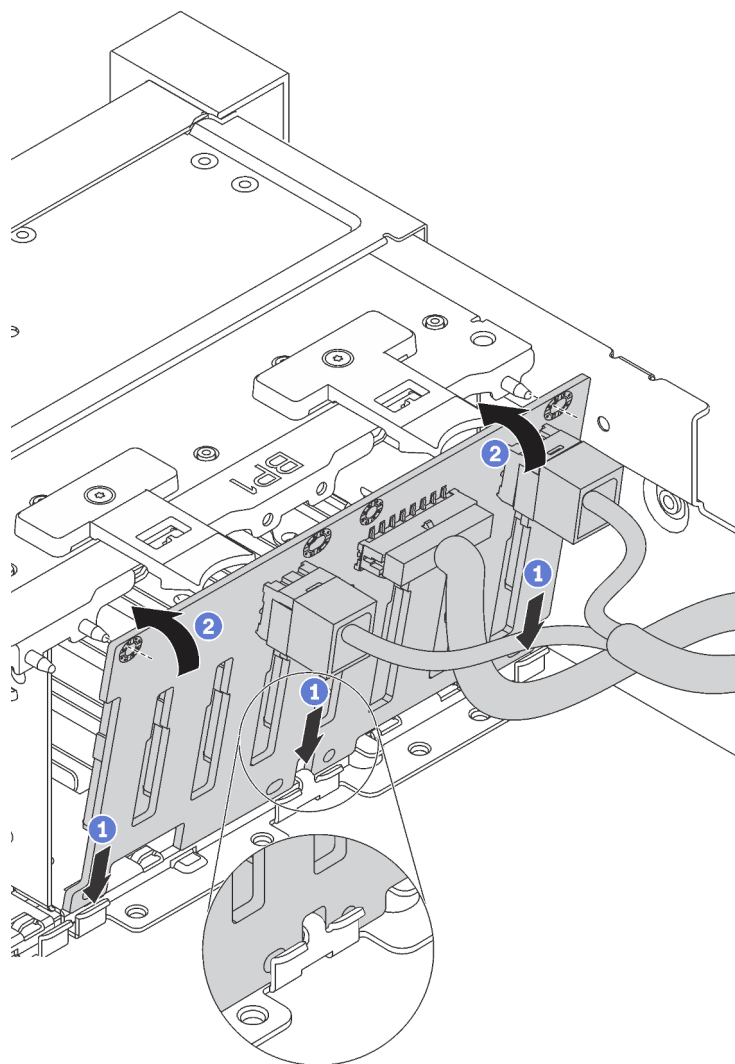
Installation d'un fond de panier d'unité 2,5 pouces
